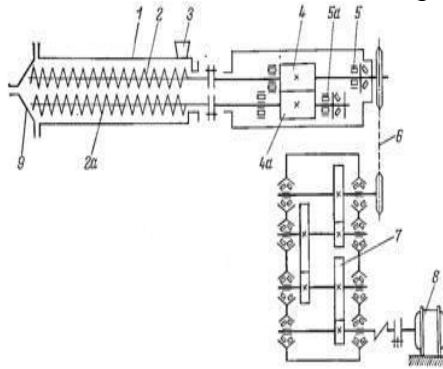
Схема двошнекового преса з паралельними шнеками: 1 – корпус; 2, 2 а – шнеки; 3 – завантажувальна воронка; 4, 4а – шестерні; 5, 5 А – наполегливі підшипники; 6 – ланцюгова передача; 7 – редуктор; 8 – електродвигун; 9 – формувальна головка
